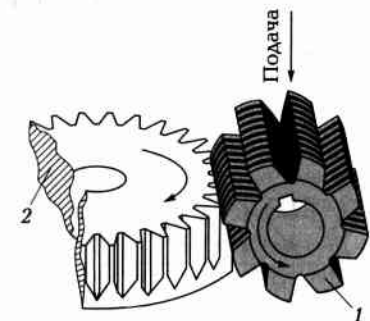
Схема нарезания зубьев червячной фрезой
